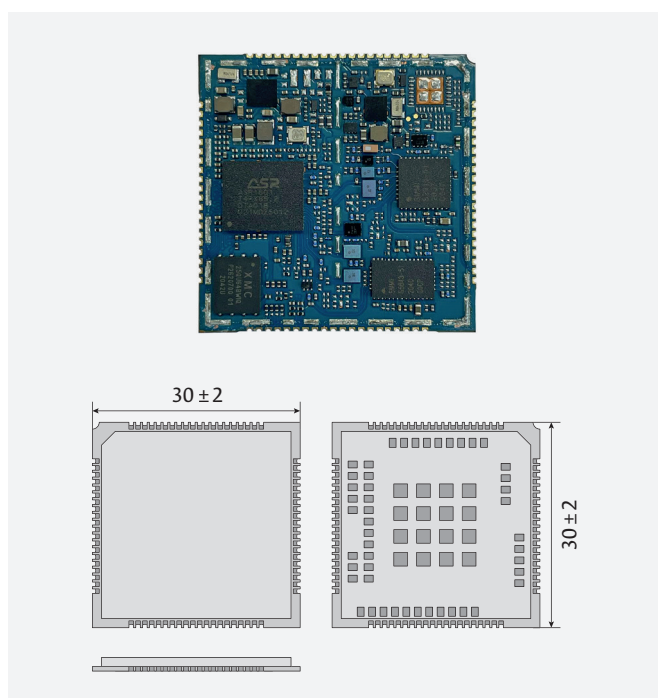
Внешний вид и размеры модуля ПР1603НБ
